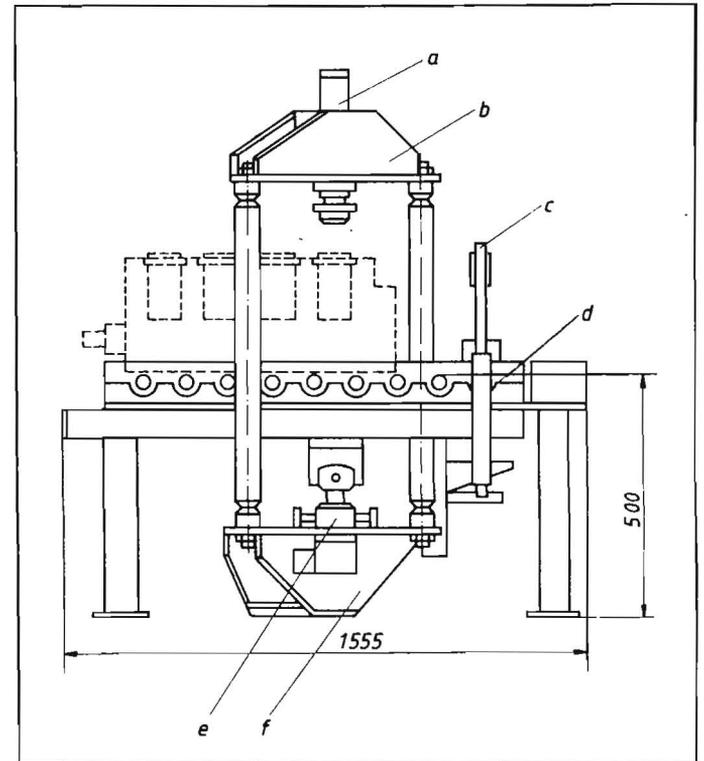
Einpreßvorrichtung für Gleitbuchsen;
